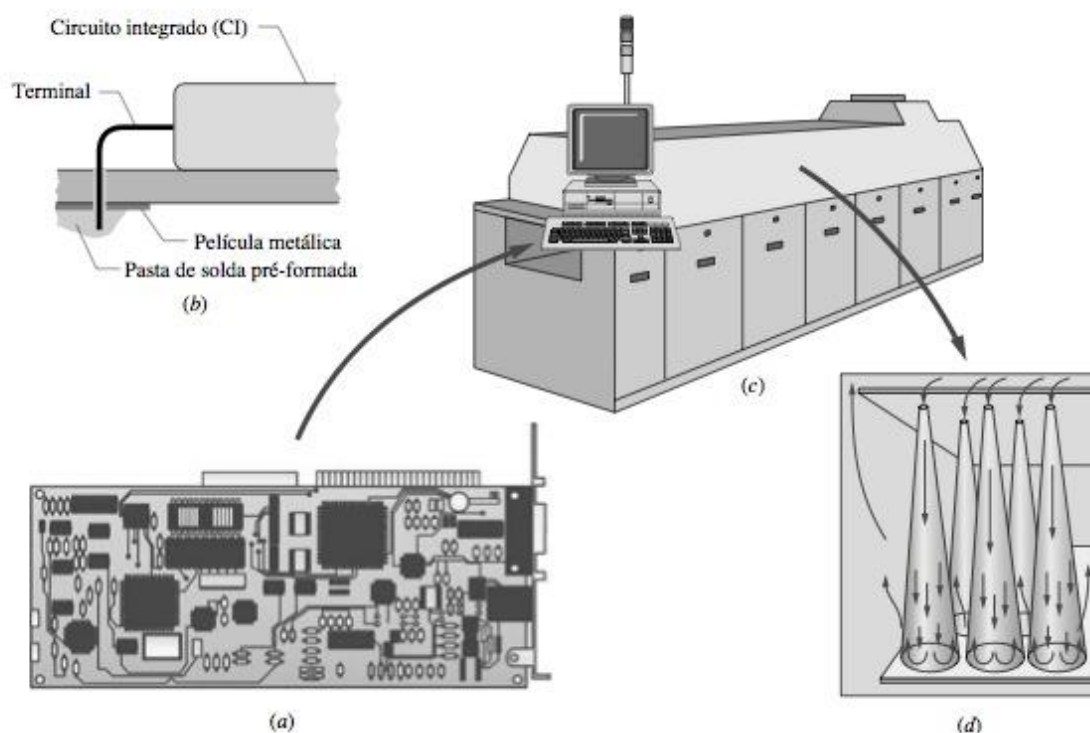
As placas de circuito impresso a serem soldadas (a) com pasta de solda pré-formada aplicada aos pinos dos circuitos integrados (b) entram no forno de soldagem por refluxo (c) em um transportador e são aquecidas à temperatura de fusão da solda por jatos de ar quente colidentes (d).
